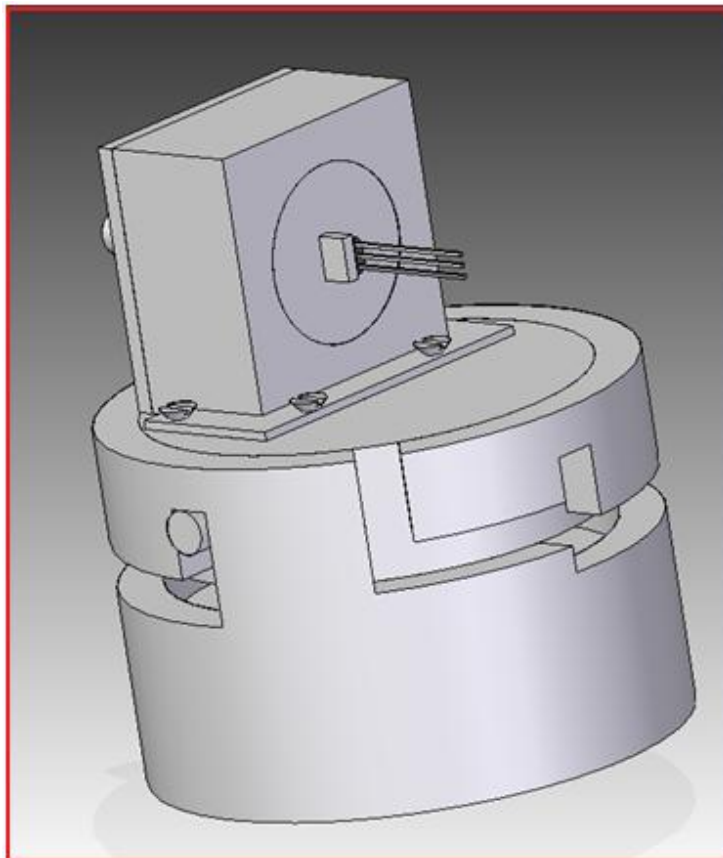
Diseño definitivo en Solid Edge de magnetómetro de muelles, posición 3
